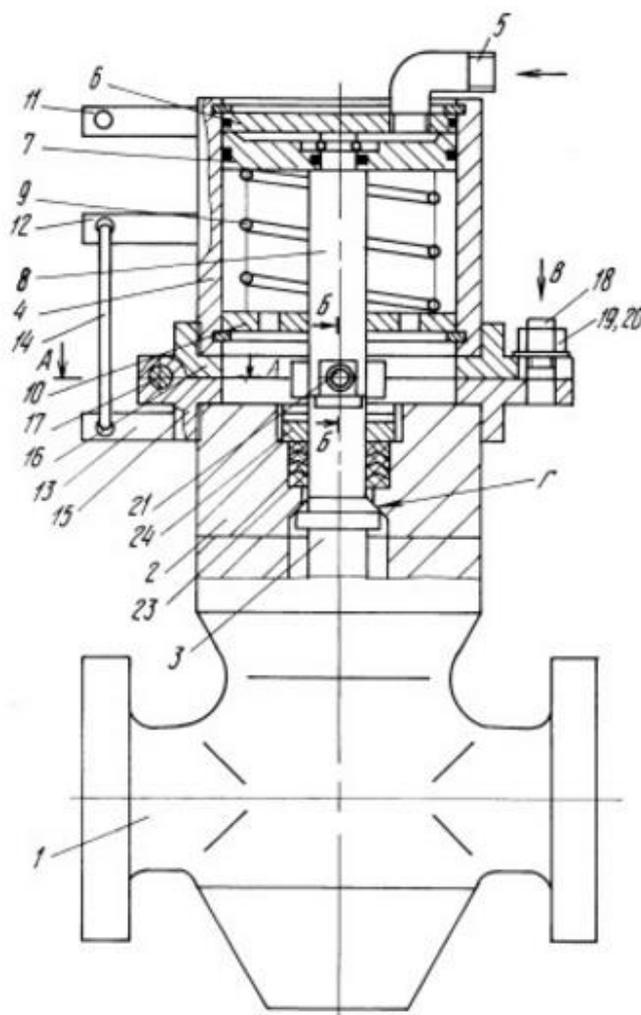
Пневмопривод задвижки в рабочем положении
